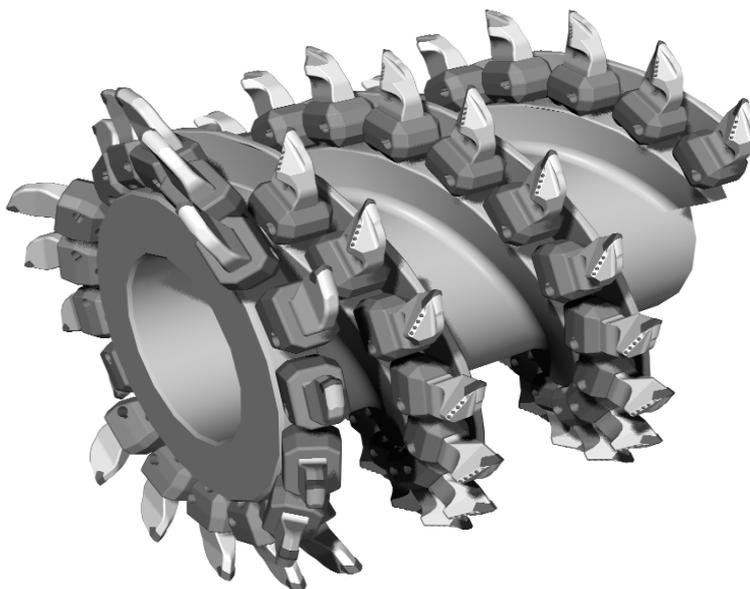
Схема расположения режущего инструмента с рабочей боковой гранью на шнеке
